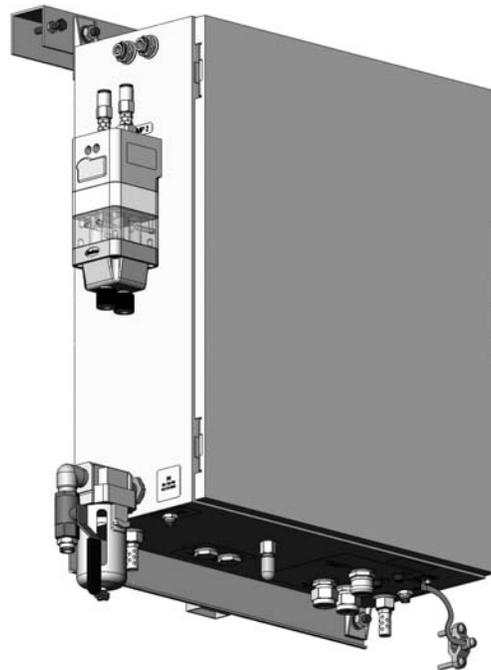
Panel de bomba (muestra una versión del sistema de dos pistolas)
